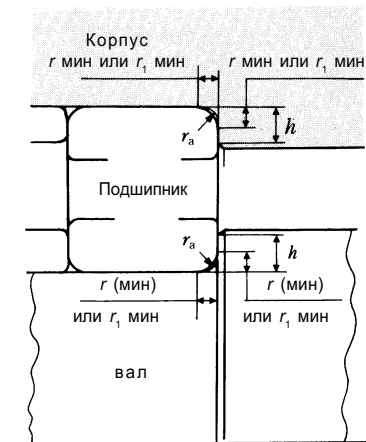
Размеры фасок, радиусы галтели вала и корпуса и высота заплечиков
